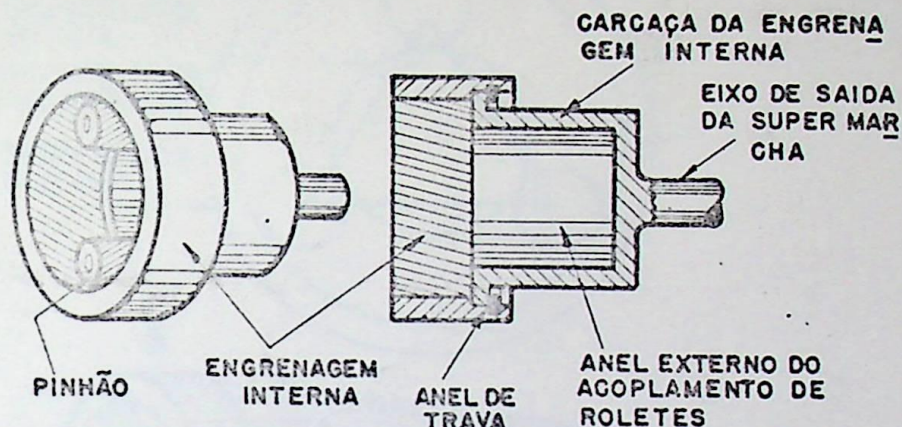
Engrenagem interna. A engrenagem interna envolve e engrena com os pinhões. A engrenagem interna é segurada pela carcaça através do anel de trava e de suas estrias.
